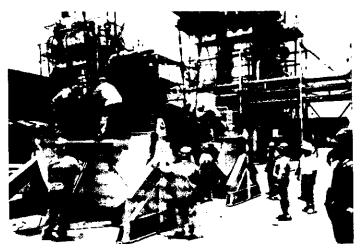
Maniobras que se realizan con el rotor de una turbina de vapor antes de realizar su montaje final.
